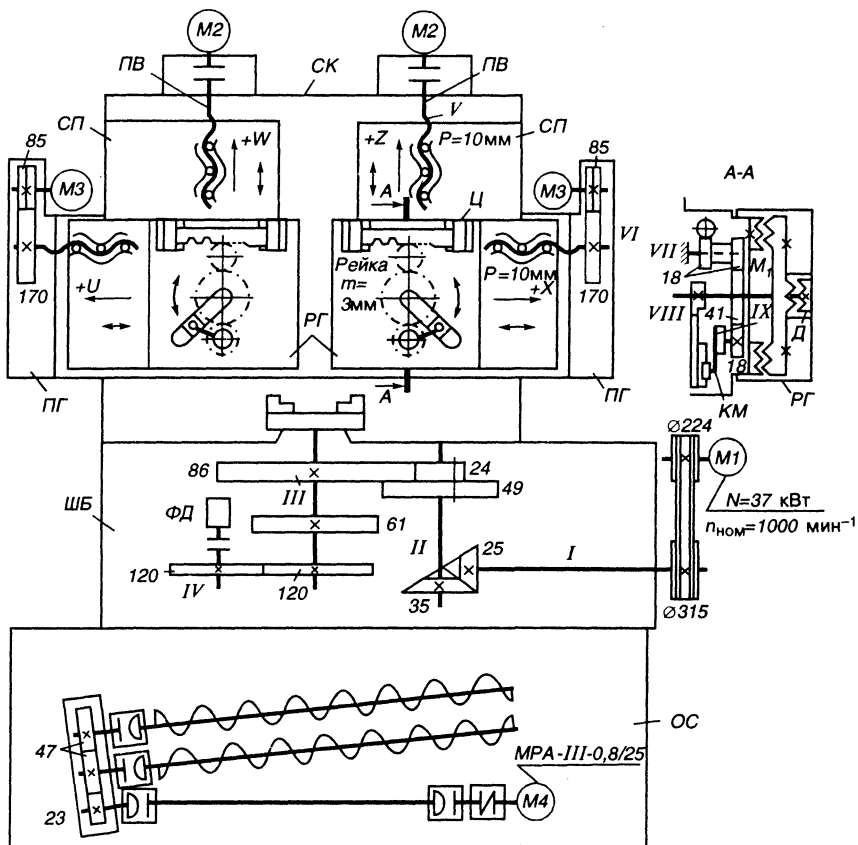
Кинематическая схема токарного одношпиндельного полуавтомата 1А734Ф3 с ЧПУ
